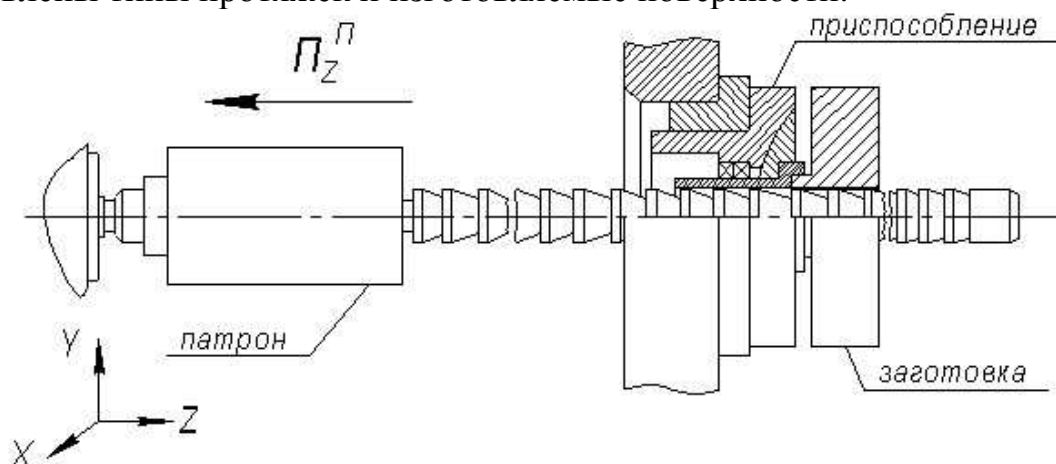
Формообразующее движение рабочих органов станка 7Б56
